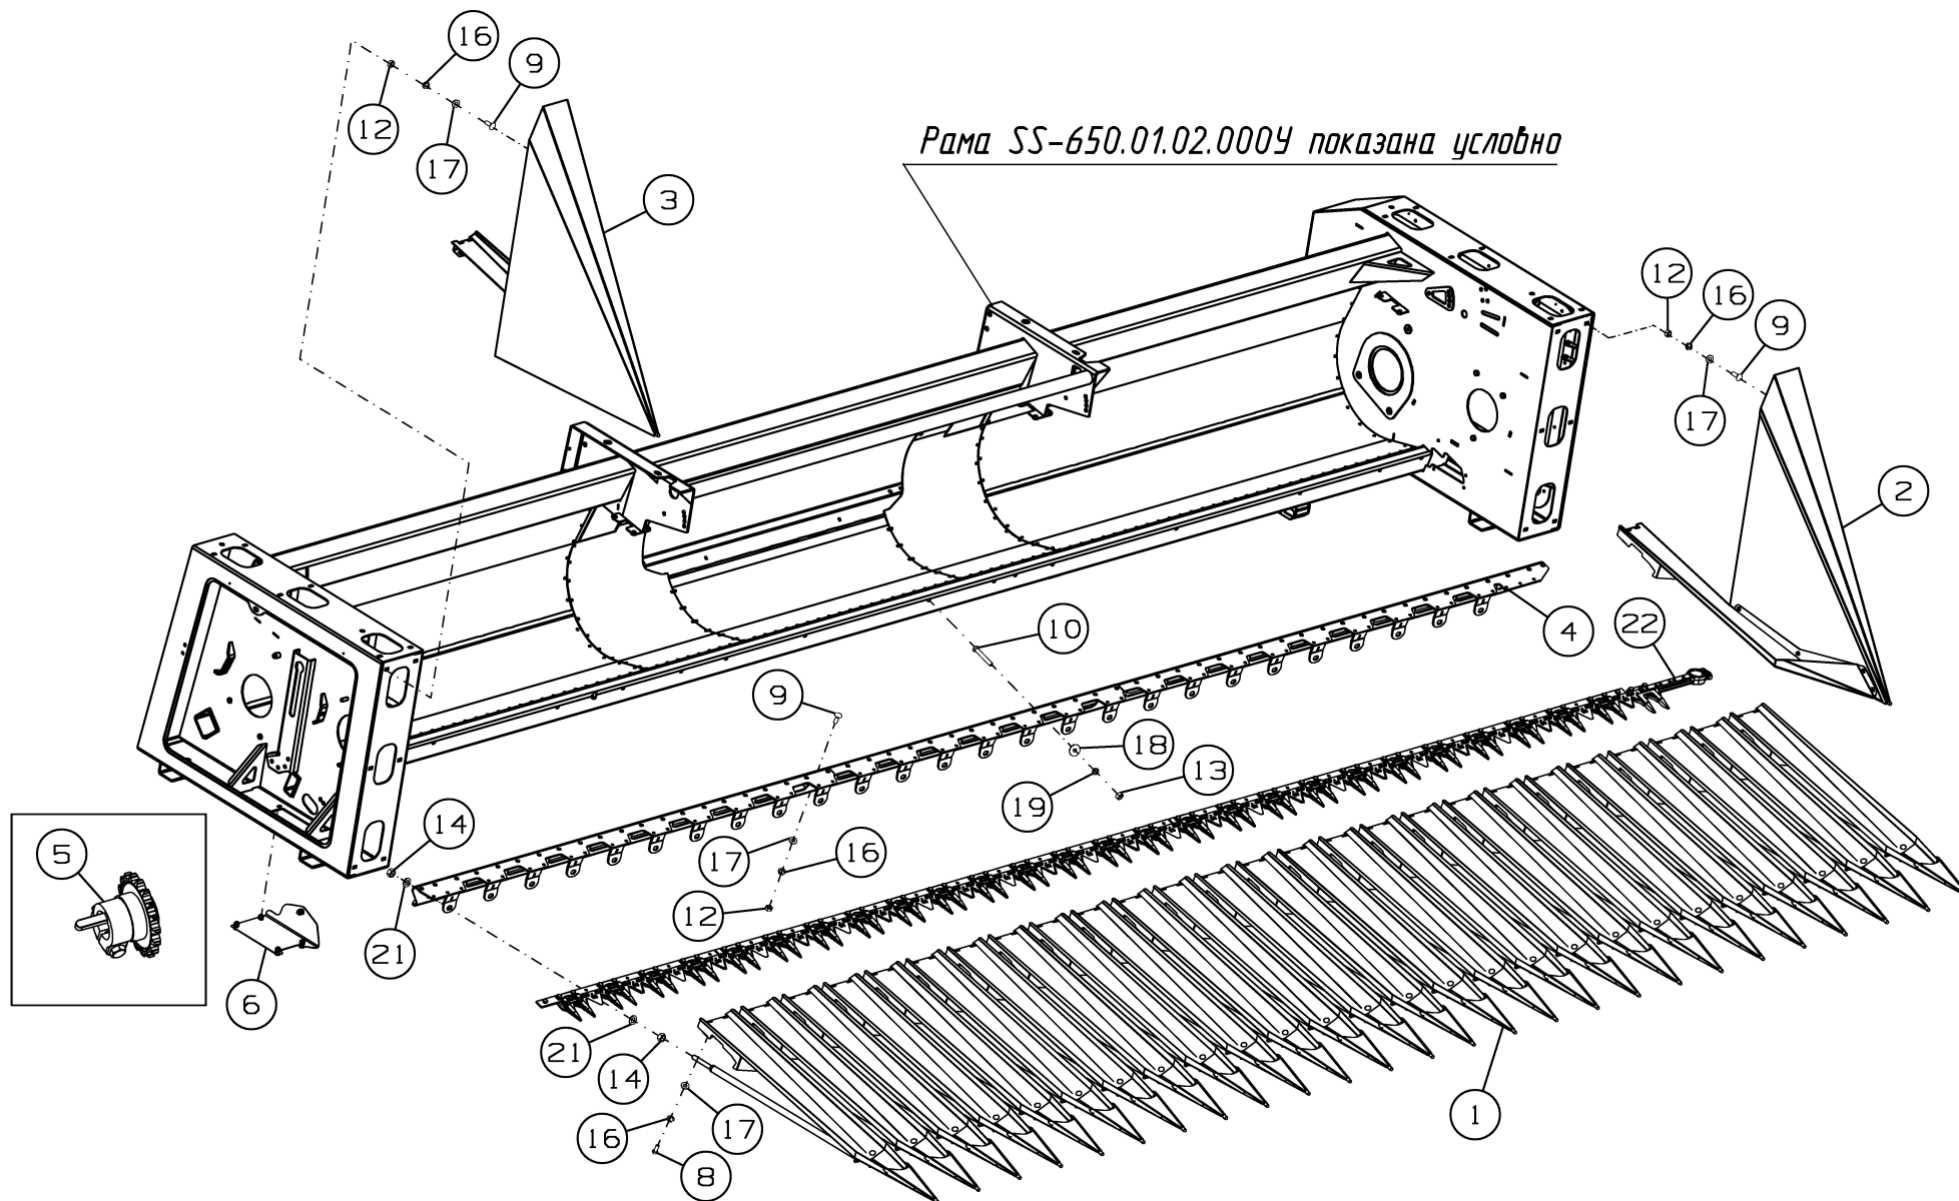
Установка делителей SS-780.01.03.000K-05
